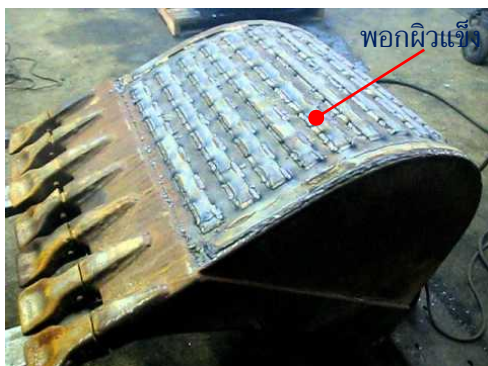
ตัวอย่างการเชื่อมพอกผิวแข็ง (Hardfacing welding)
